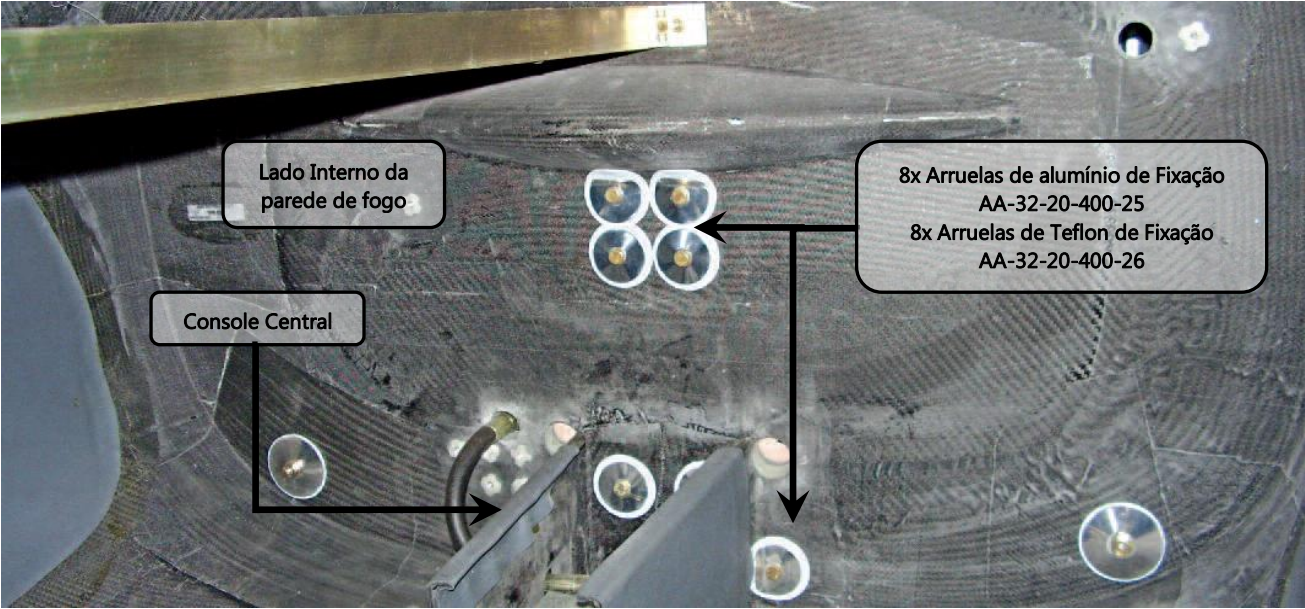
Detalhe da fixação da Estrutura (interior da cabine).
